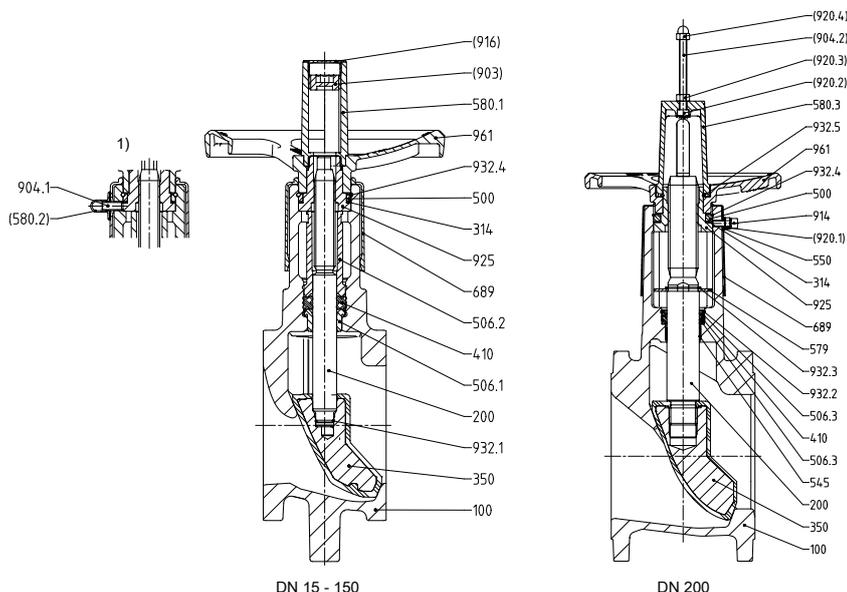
Vistas de sección; 1) dibujadas giradas 90°
